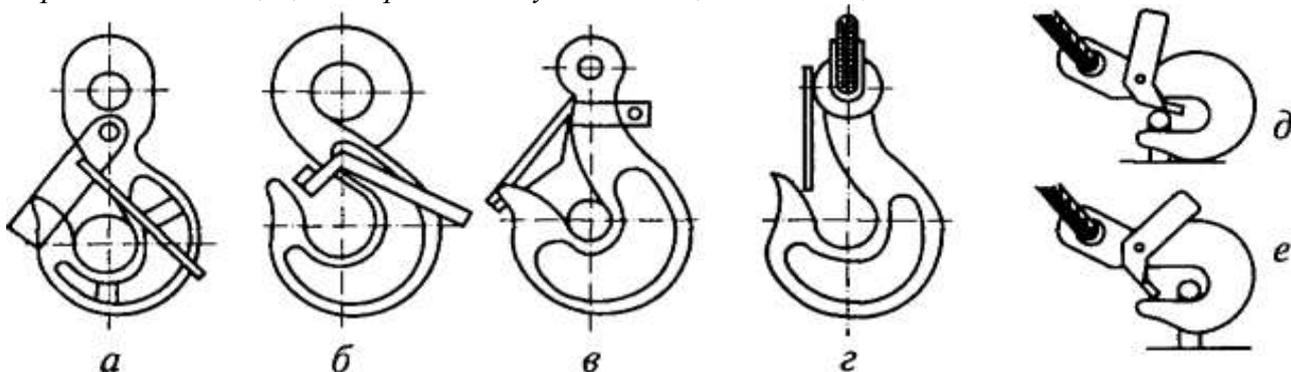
Крюки с предохранительными устройствами (а — с предохранительной планкой; б — с предохранительной скобой; в — с поворотным козырьком; з — с предохранительной пружиной) и установка крюка в проушине (д — неправильная установка; е — правильная установка)
